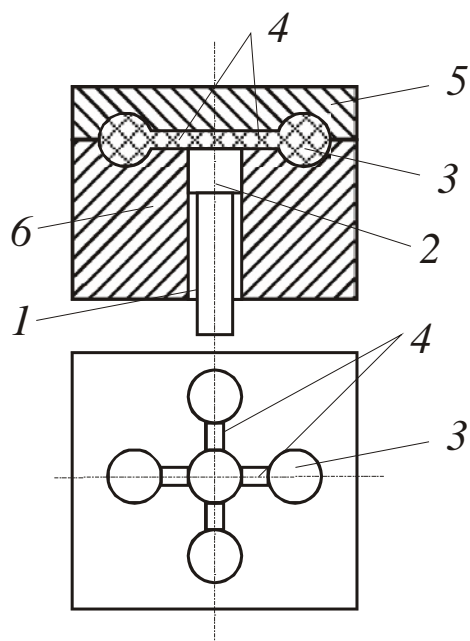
Схема трансферного прессования с нижней загрузочной камерой:
